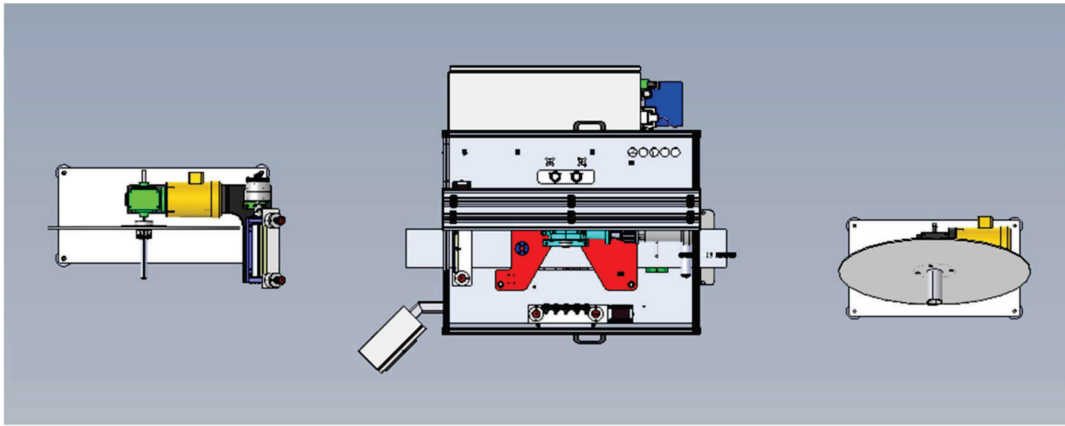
(Layout) Desenho do equipamento – Vista superior
